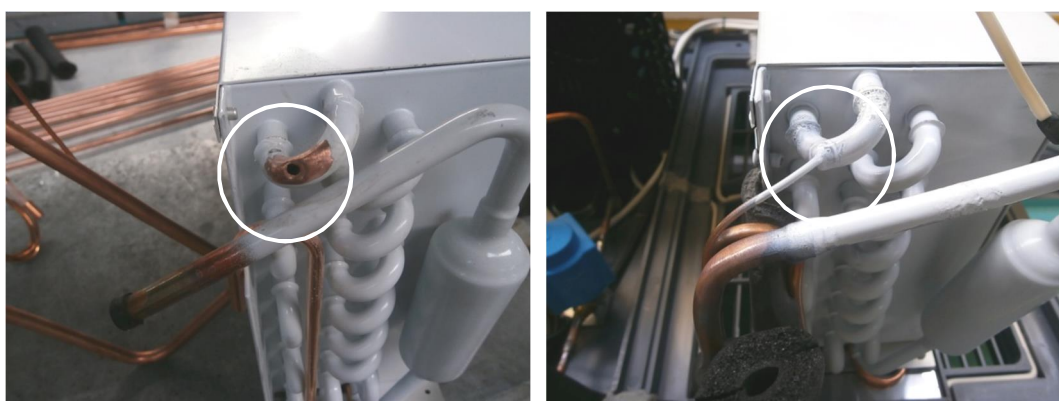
Operação de soldadura capilar - evaporador
